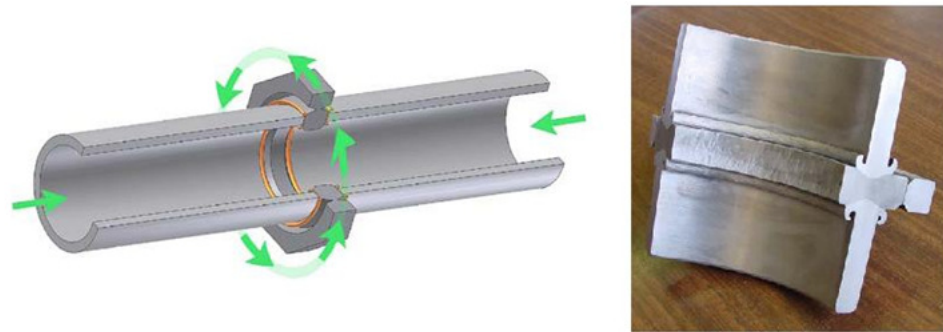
Soldagem por fricção em tubulações longas<sup>(30)</sup>.
